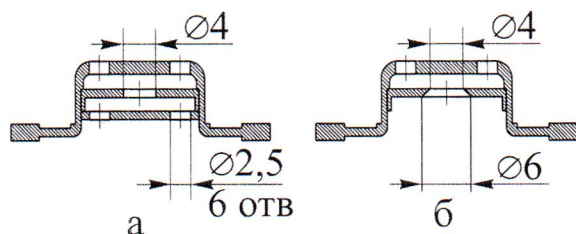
Чертежи сеточного узла газоразрядного прерывателя тока: а – с двумя областями сужения на пути горения разряда, б – с коническим отверстием в управляющем электроде
